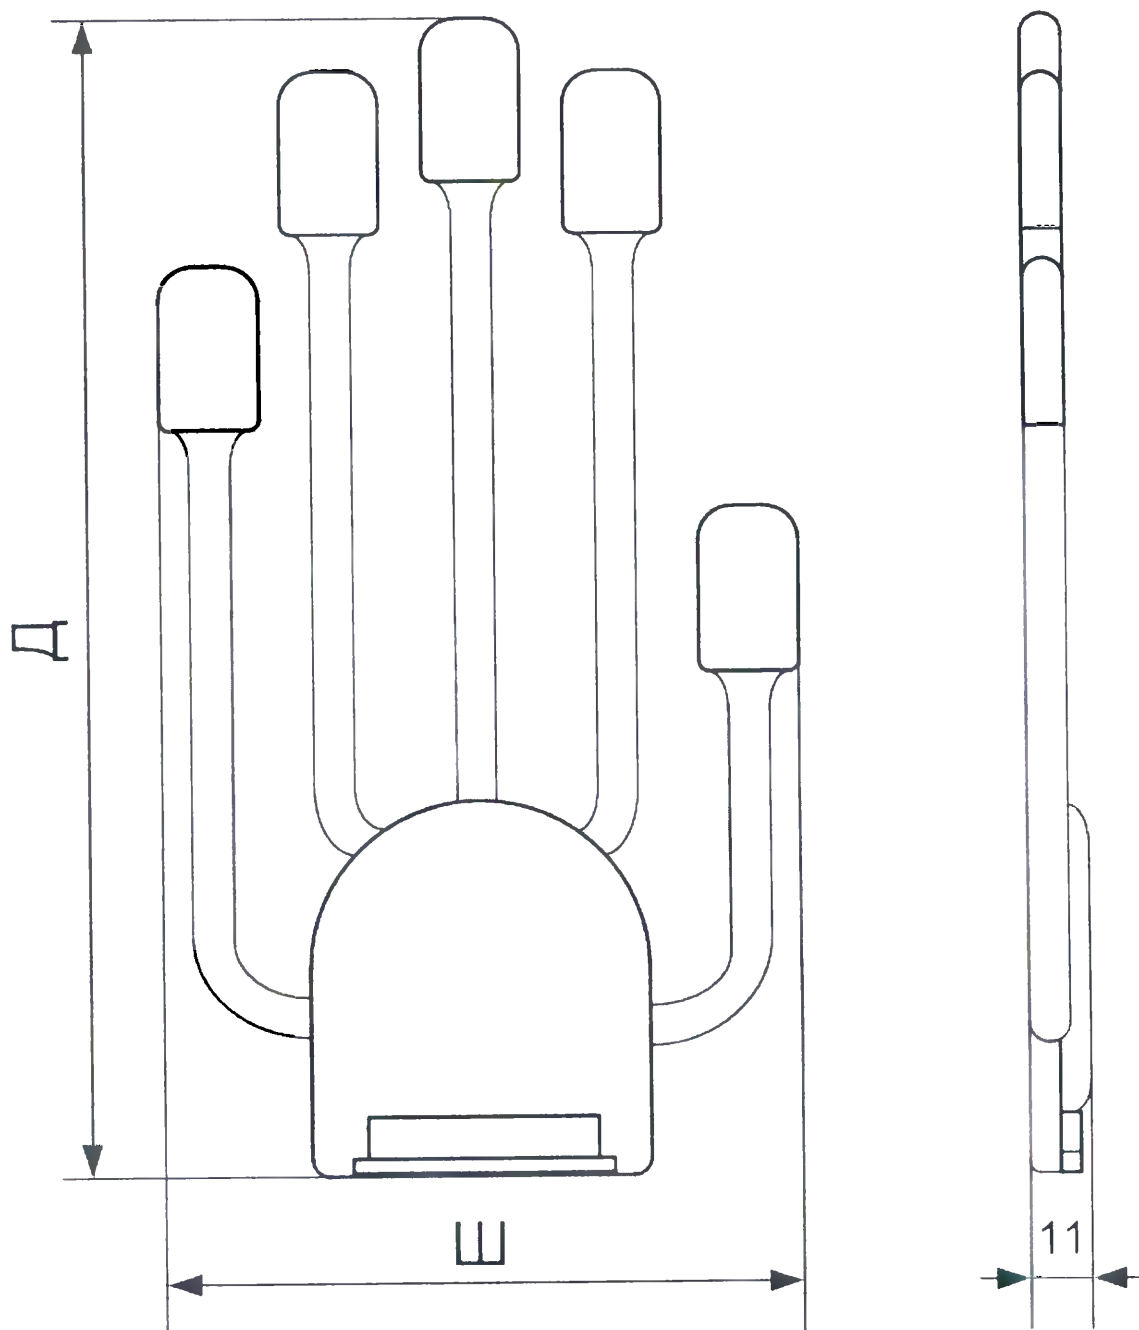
Габаритные размеры блока датчиков комплекса модификаций
